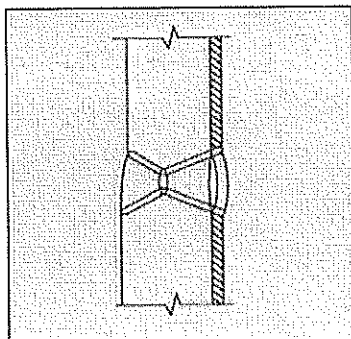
Diseño de junta de soldadura circunferencial.
